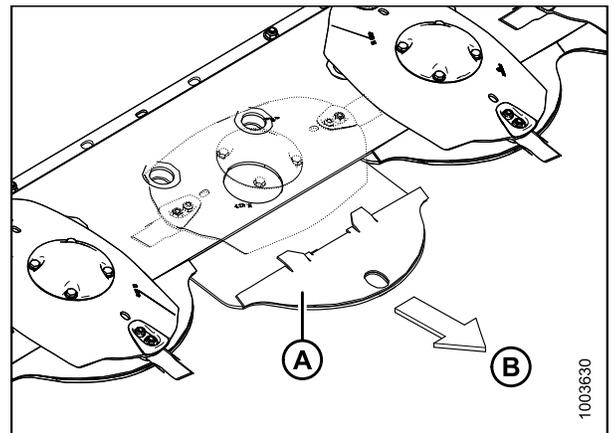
Jupe pare-pierres retirée de la barre de coupe
